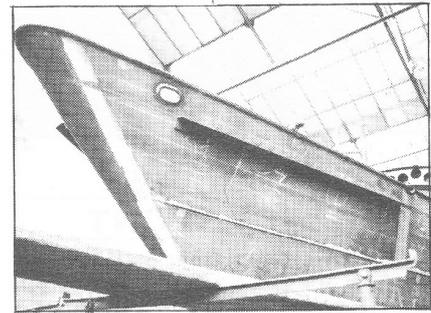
Cornière de tenue des tôles lors du soudage du pont au pavois, au chantier Meta.
